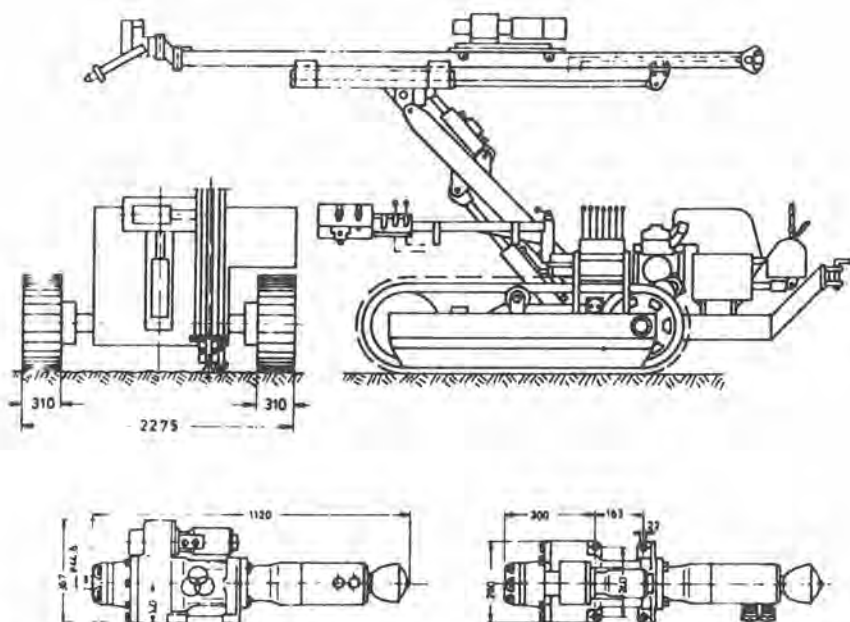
Øverst — Krupp DHR 75 helhydraulisk borenhet montert på selvgående beltevogn. Nederst — Krupp hydraulisk borhammer type HB101 — HB103.
